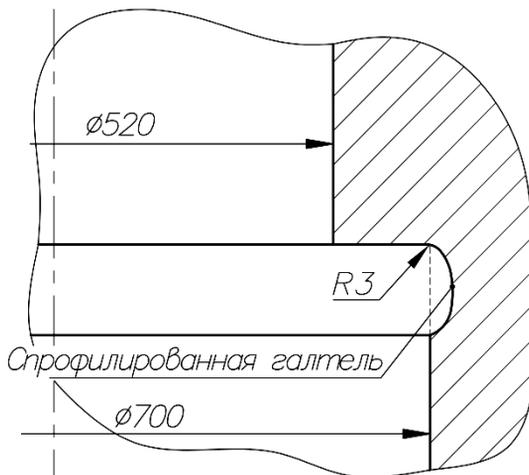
Конструкция галтельного перехода с заглаблением в вертикальную стенку отверстия для установки гайки нажимного винта
